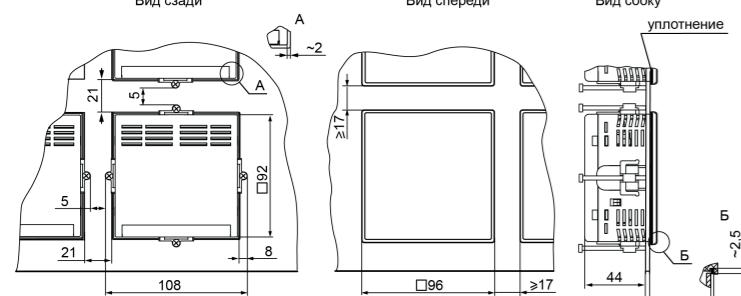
Корпус Щ1 в щите толщиной 3 мм
